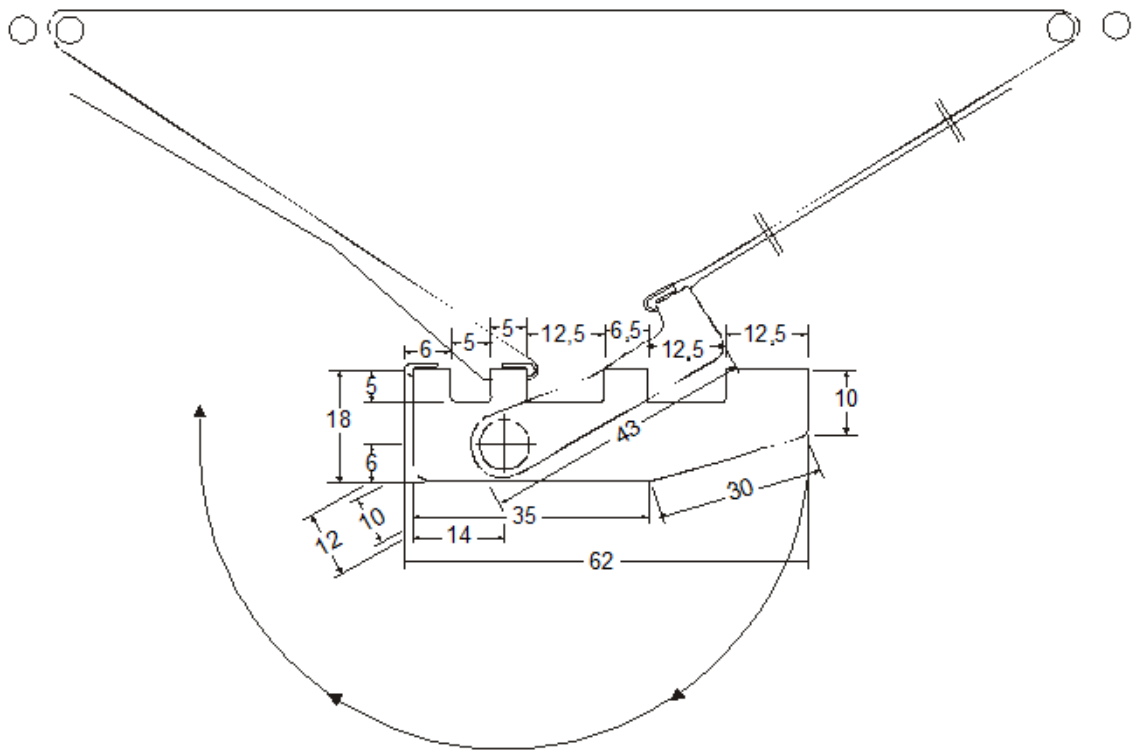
Vista da fivela tensora aberta (medidas em mm)
